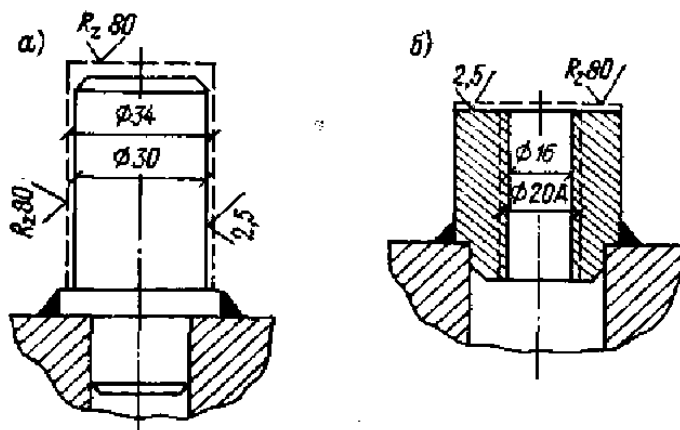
Схема установки фиксаторов с припуском для обработки после сварки:
